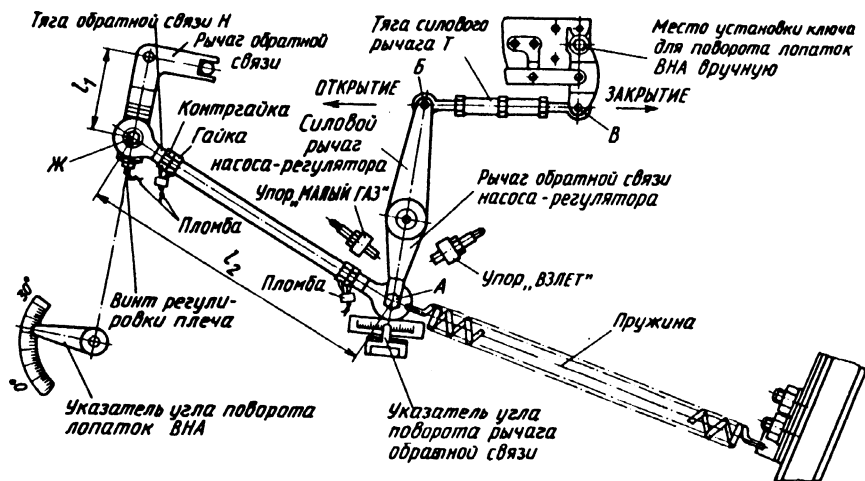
Схема расположения тяг обратной связи регулятора направляющих аппаратов компрессора
